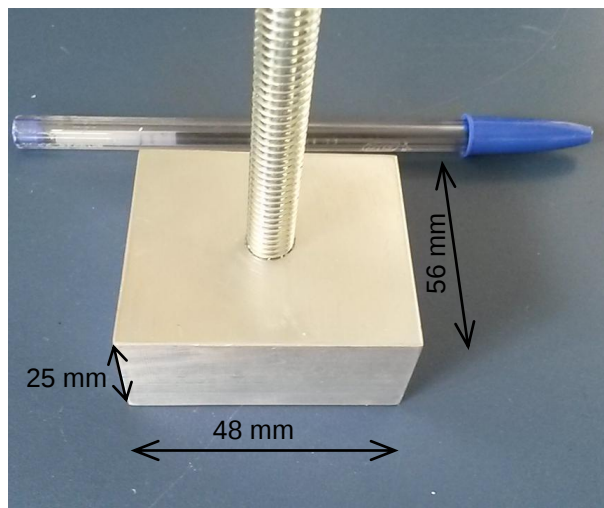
Sapata utilizada para aplicação de carga no ensaio.
